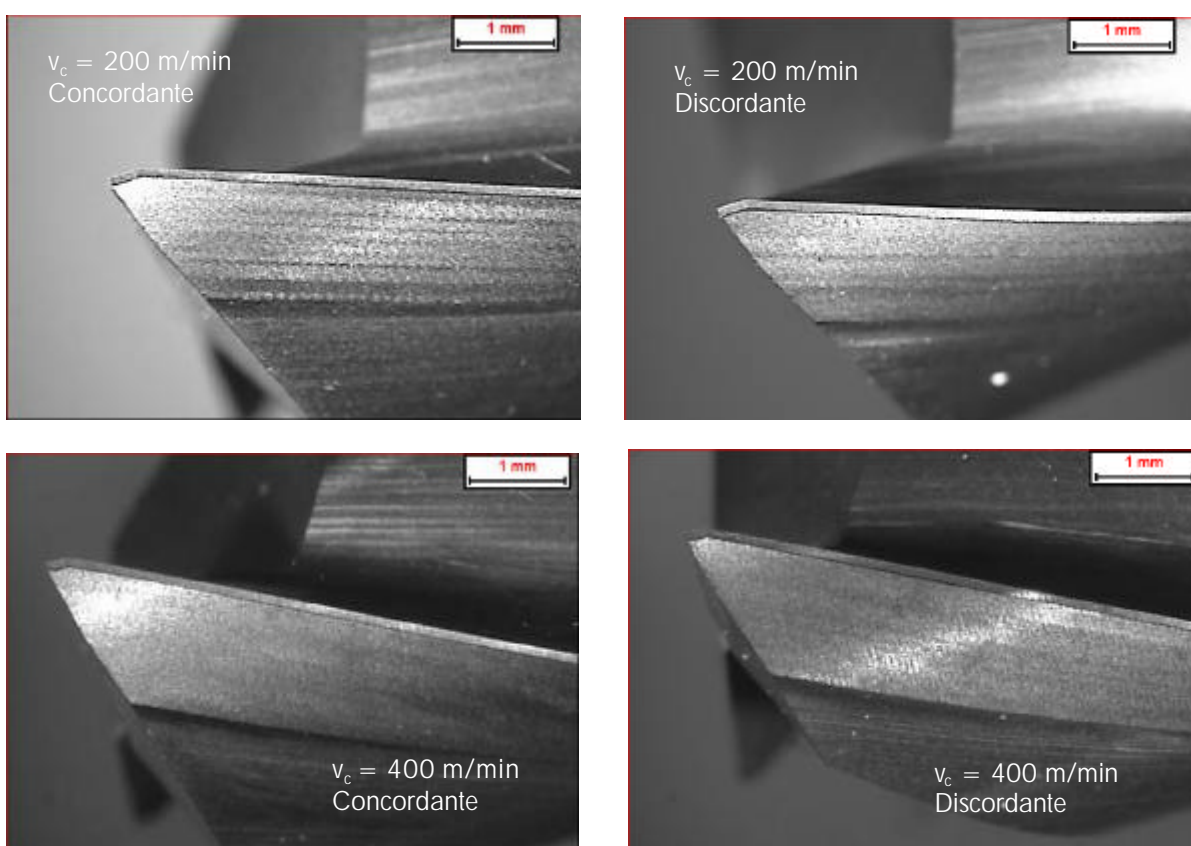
Desgaste de flanco uniforme para $VB = 0,1$ mm.
